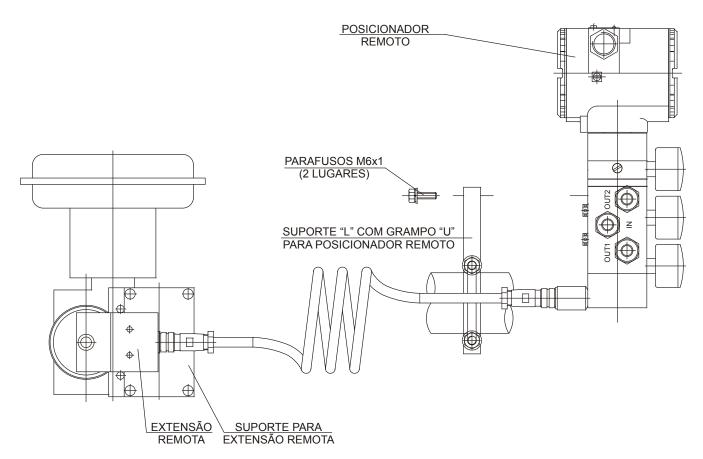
Posicionador em Atuador Rotativo com Sensor de Posição Remoto
